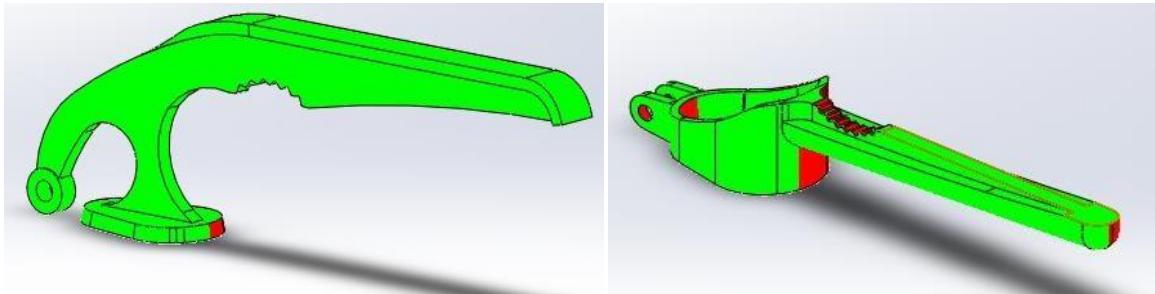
Pièce haut et pièce bas après dépouille.
